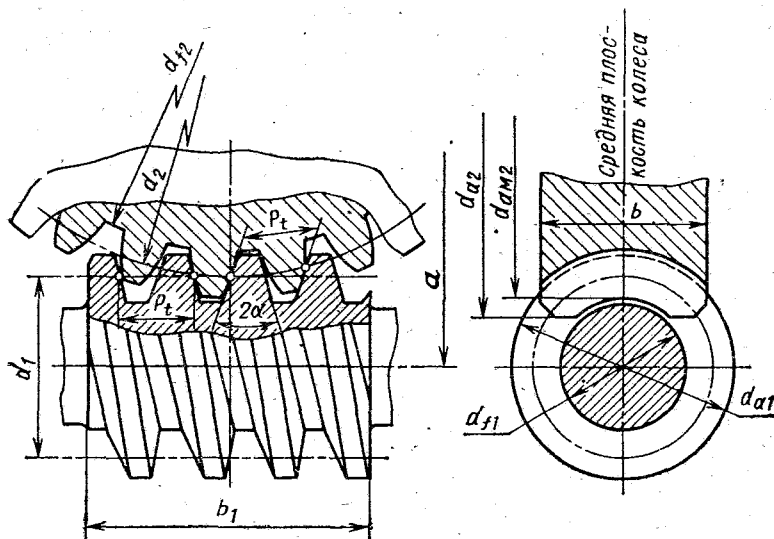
Элементы цилиндрического червяка и червячного колеса
